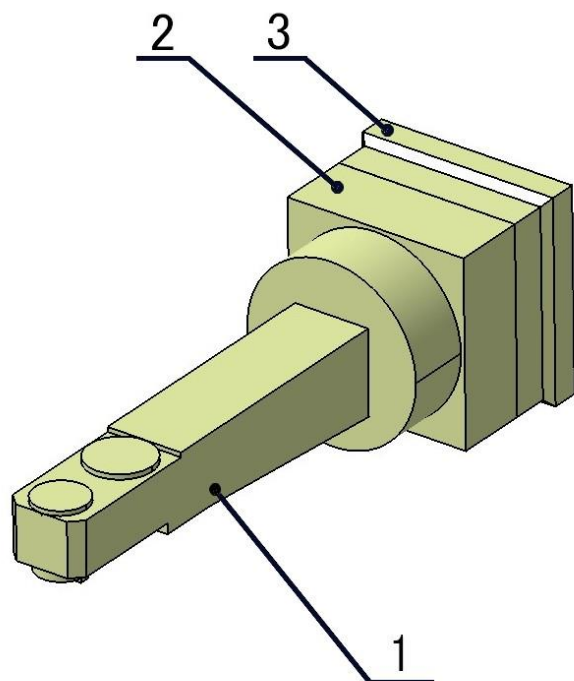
Frézovací zařízení IFVW 103 – Řez [6]
